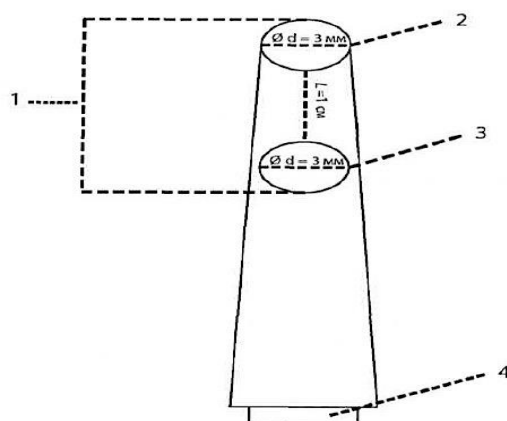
Насадка інструменту для забору частини ЩЖТ
